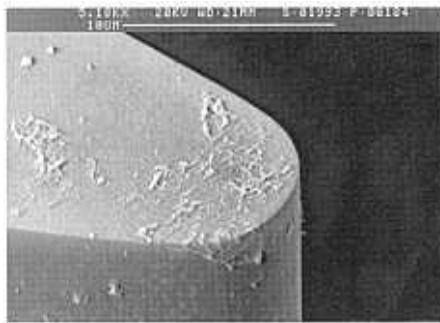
Diamantdrehwerkzeug. (Bild: IPT)
